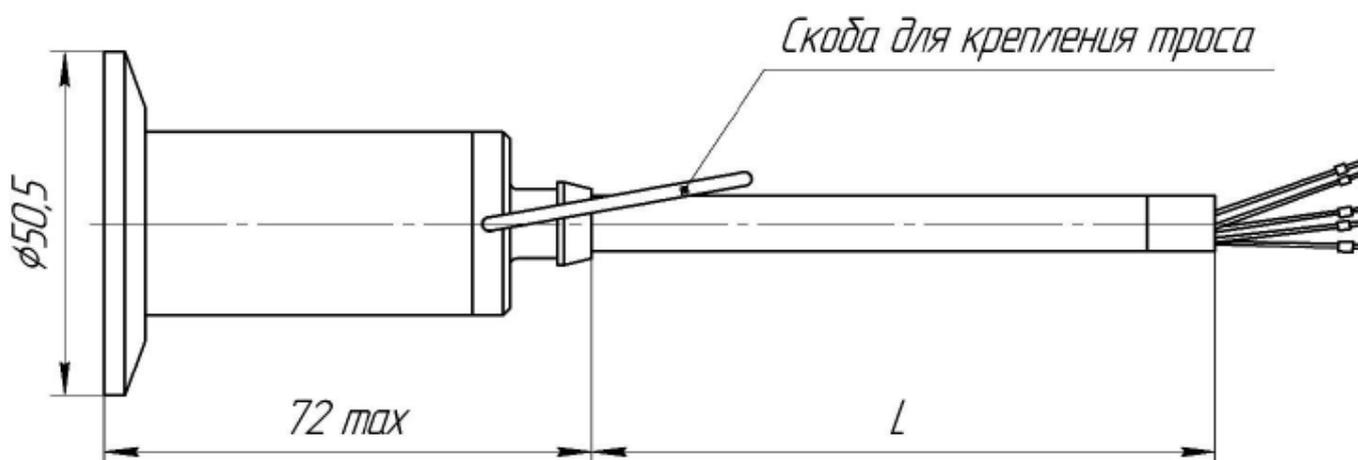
Габаритный чертеж преобразователей гидростатического давления с кодом D20, кодом присоединительного размера 5 и кодом конструктивного исполнения K05
